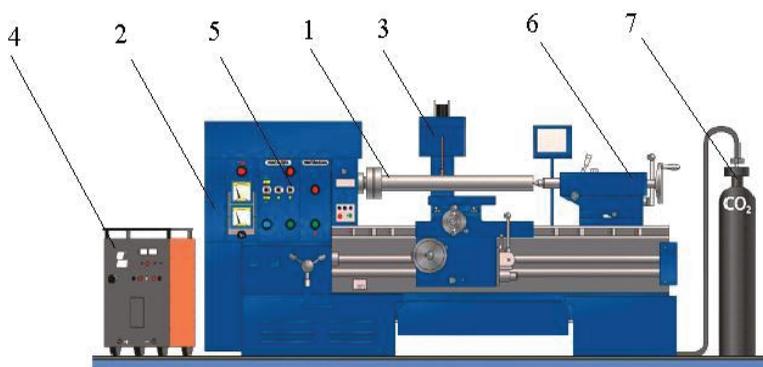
Схема типовой установки для автоматической наплавки цилиндрических деталей порошковой проволокой: 1 – наплавляемая деталь; 2 – манипулятор-вращатель; 3 – сварочная головка; 4 – источник питания; 5 – пульт управления; 6 – задняя бабка; 7 – баллон с защитным газом
